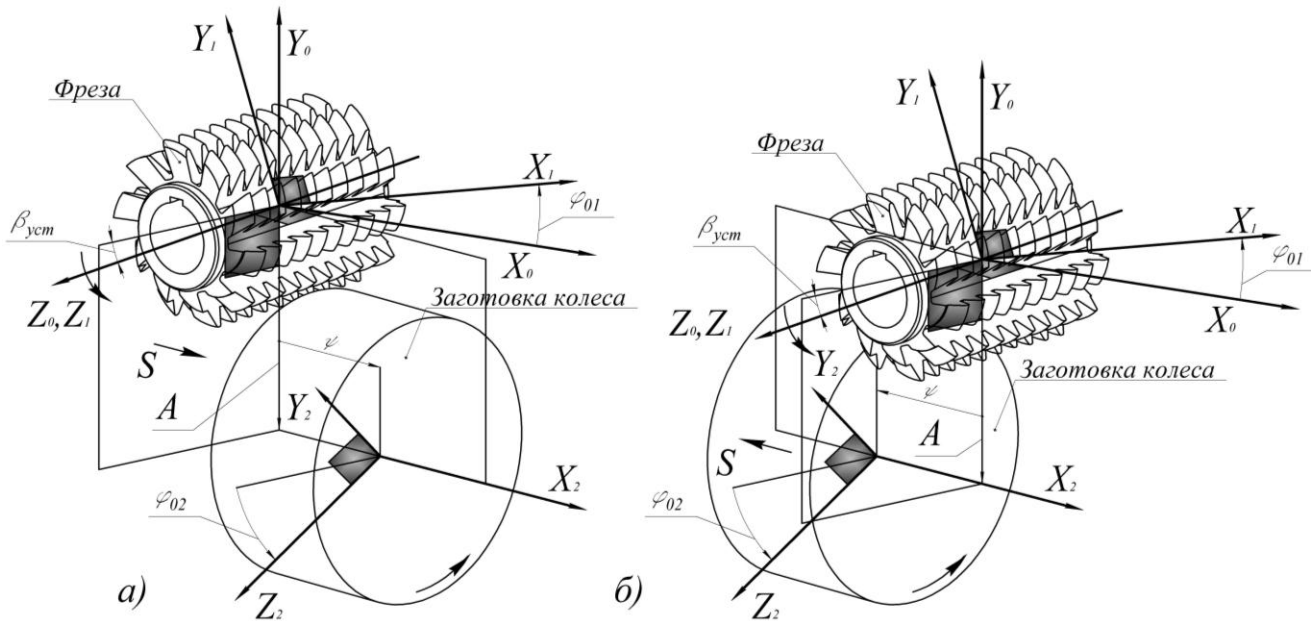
Розташування систем координат при зубофрезеруванні: а) зустрічна подача; б) попутна подача
